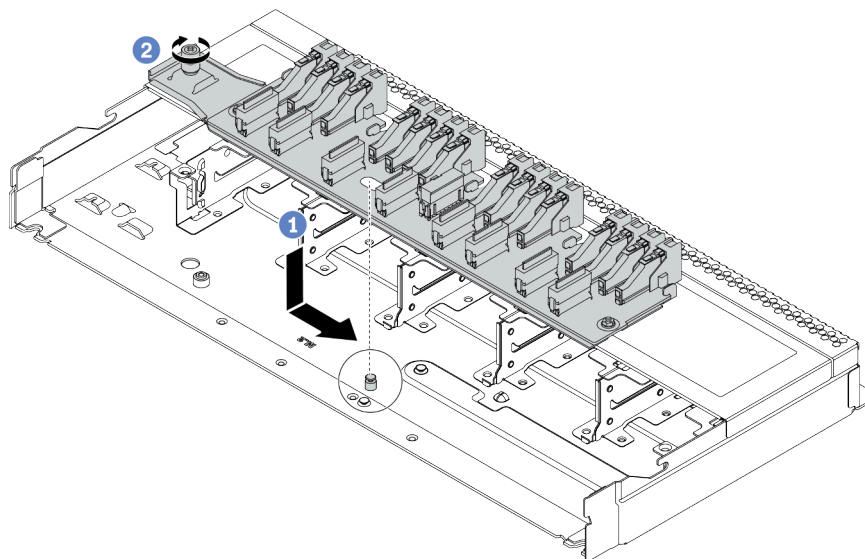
Installation d'un fond de panier pour 16 unités EDSFF
